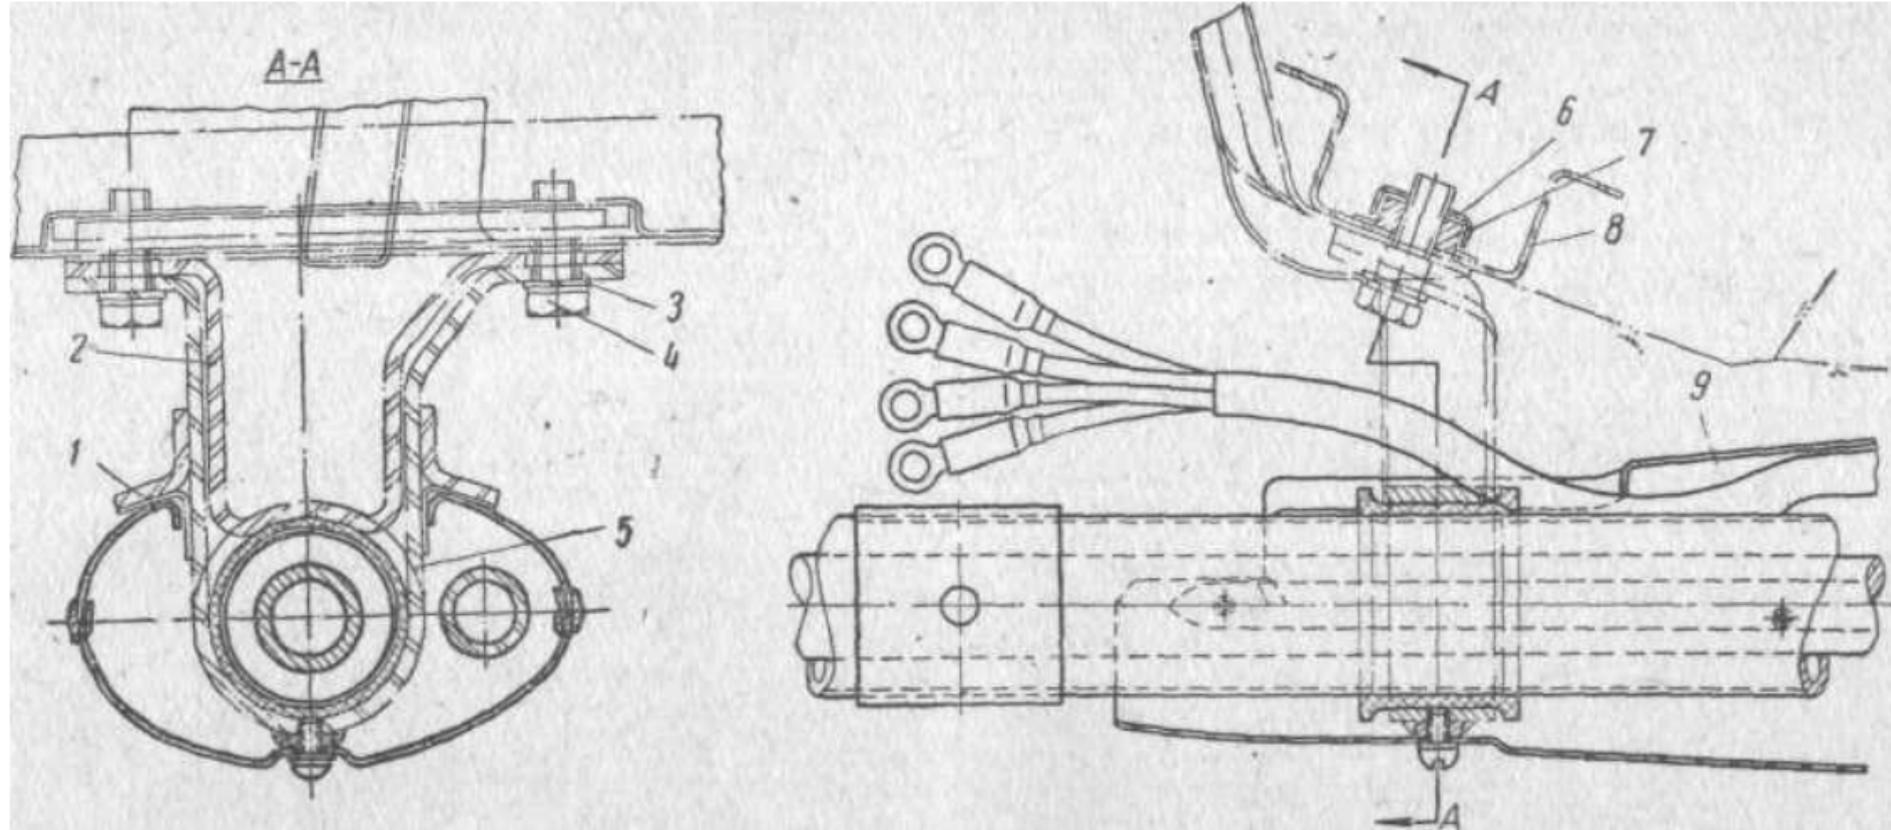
Крепление рулевой колонки автомобиля модели 407 и ее кожуха к кузову:
